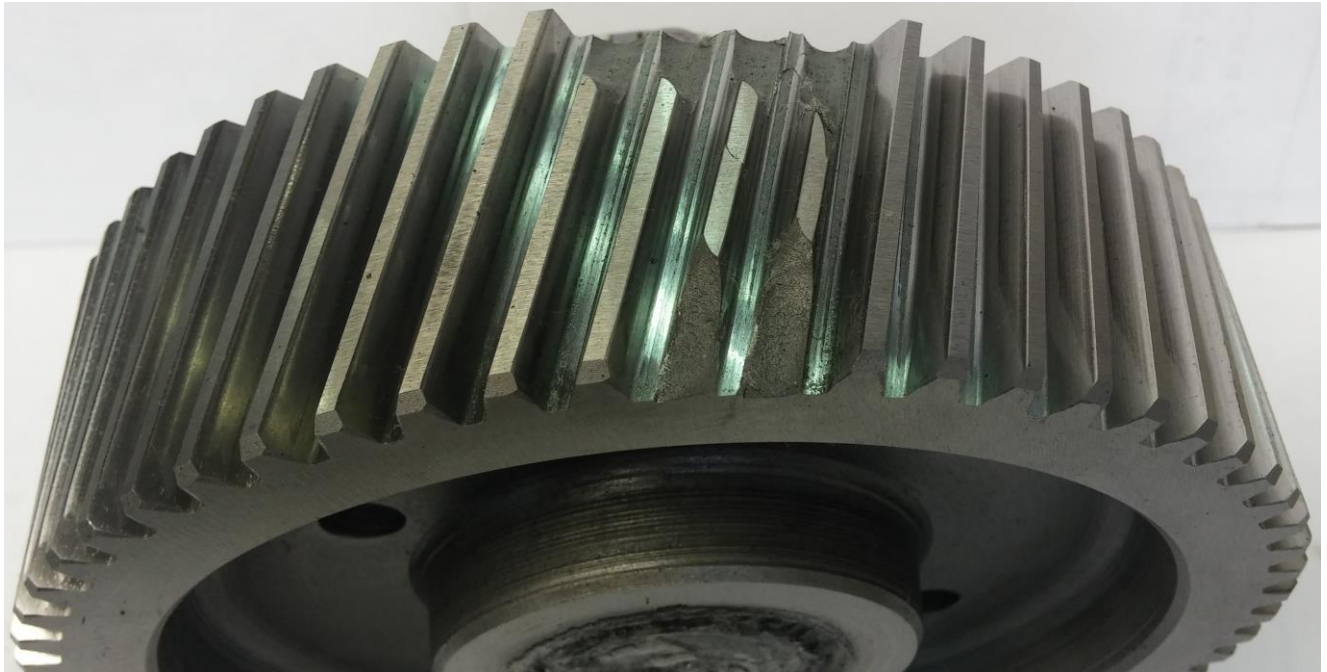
Внешний вид колеса первой ступени редуктора с эвольвентным зубчатым зацеплением после испытаний
